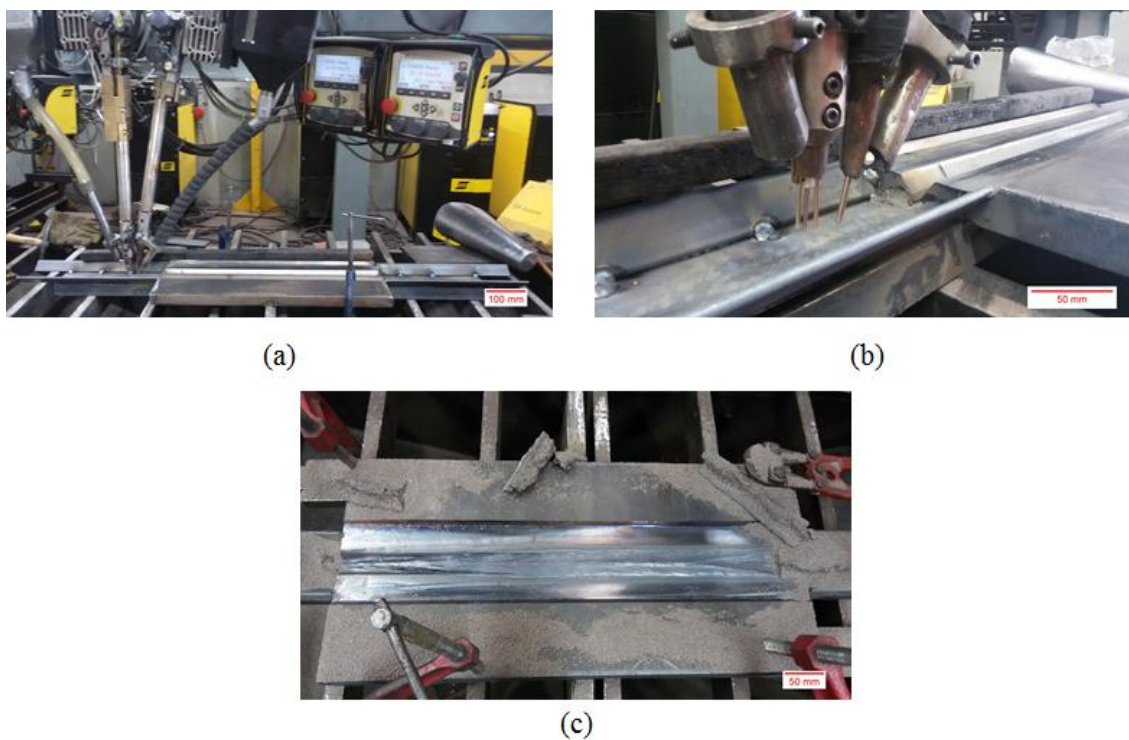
Etapas do processo de soldagem: a) posicionamento da chapa e ajuste do equipamento; b) detalhe do alinhamento das tochas; c) remoção da escória.
